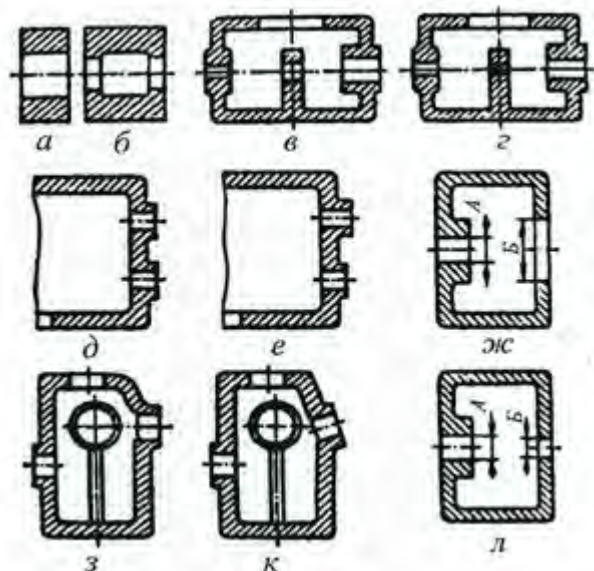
Приклади конструкцій деталей машин, оброблених на розточувальних верстатах
